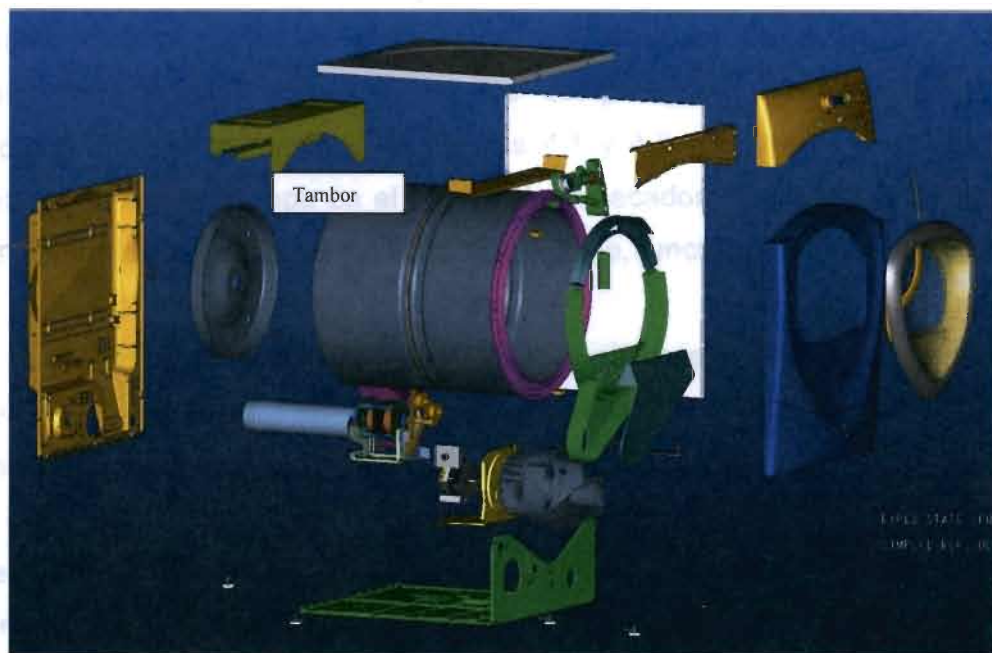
Explosionado de Partes de la Secadora a Manufacturar.
